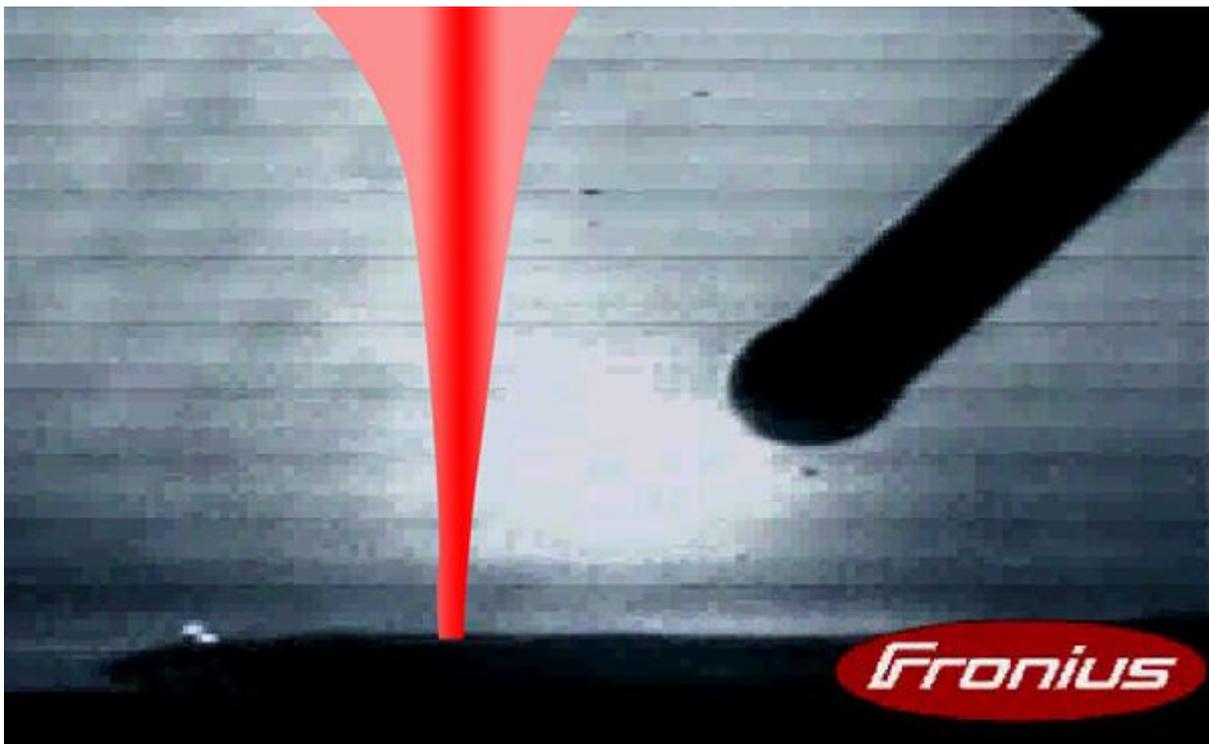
Схематическое изображение процесса сварки Laser-GMAW
